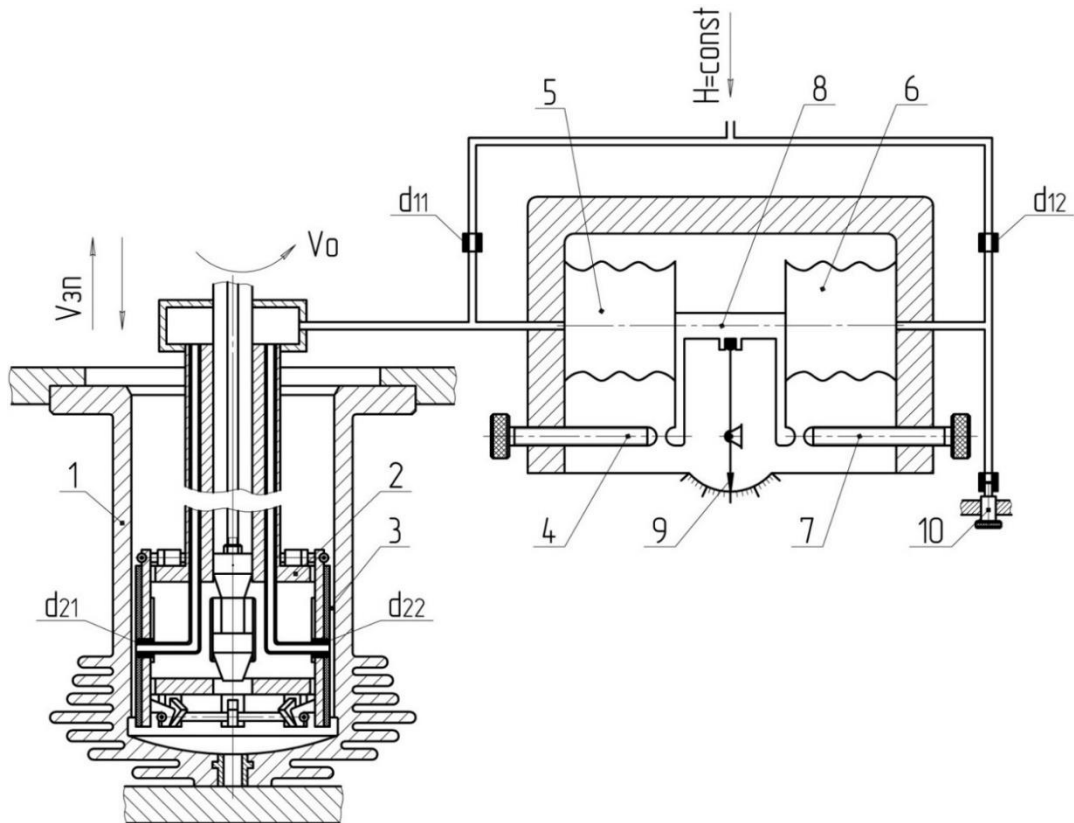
Схема безконтактного пневматичного вимірювального пристрою безперервного контролю, що вбудована в хонінгувальну головку: 1 – заготовка; 2 – корпус хонінгувальної головки; 3 – абразивний брусок; 4 – контакти лівого сиффону; 5 – лівий сиффон; 6 – правий сиффон; 7 – контакти правого сиффону; 8 – мостик; 9 – шкала із стрілкою; 10 – регулюючий дросель; d_{11} і d_{12} – вхідні сопла; d_{21} і d_{22} – вимірювальні сопла
